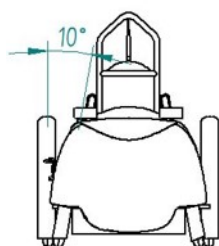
Desenho técnico da vista frontal do protótipo GP17 EVO
